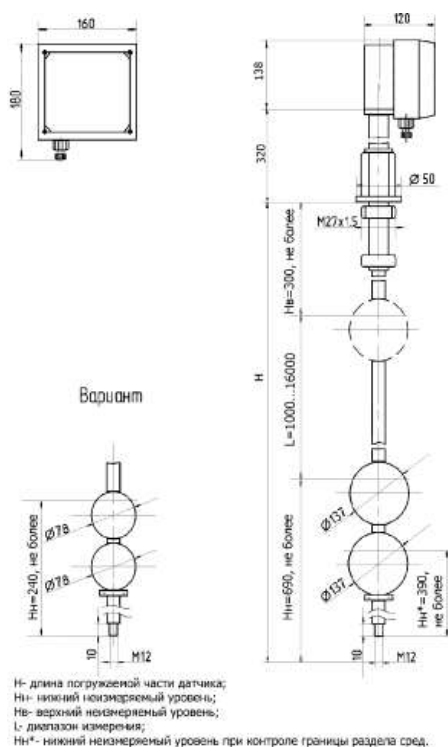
Габаритные и присоединительные размеры преобразователя передающего (ППР)
